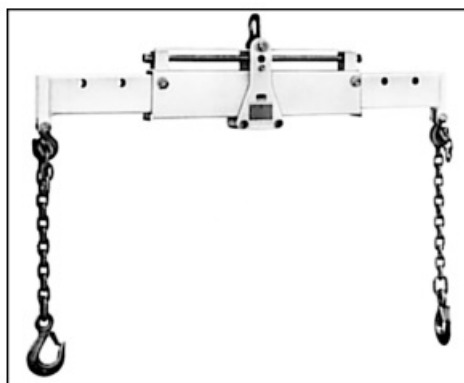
Стропи для транспортування двигуна Load-Rotor OEM4130
